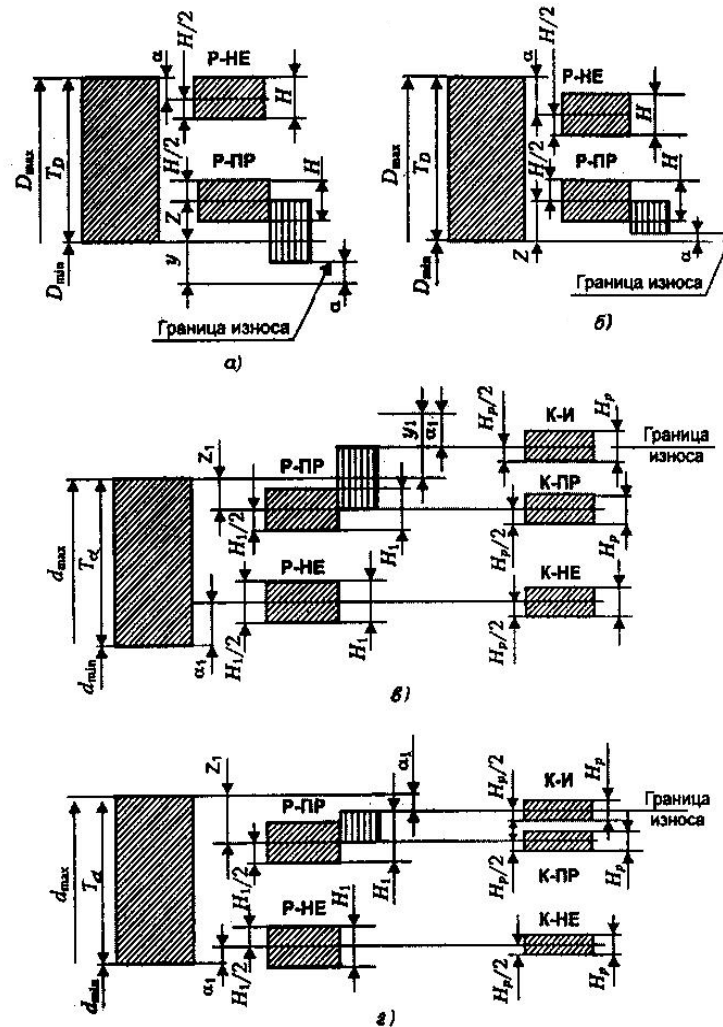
Схемы расположения допусков калибров для номинальных размеров св. 180 до 500 мм: а – для отверстий IT6 – IT8; б – для отверстий IT9 – IT17; в – для валов IT6 – IT8; г – для валов IT9 – IT17
